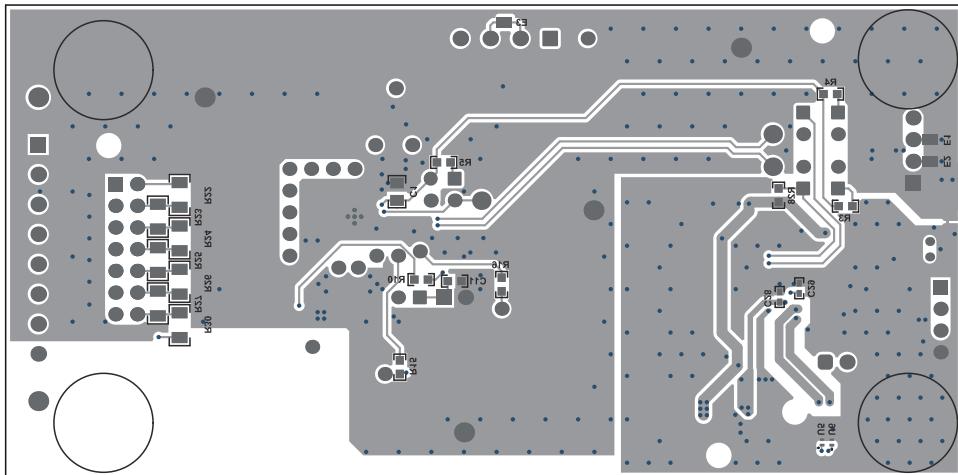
BQ77307 Two-Layer Board Layout—Bottom Layer
